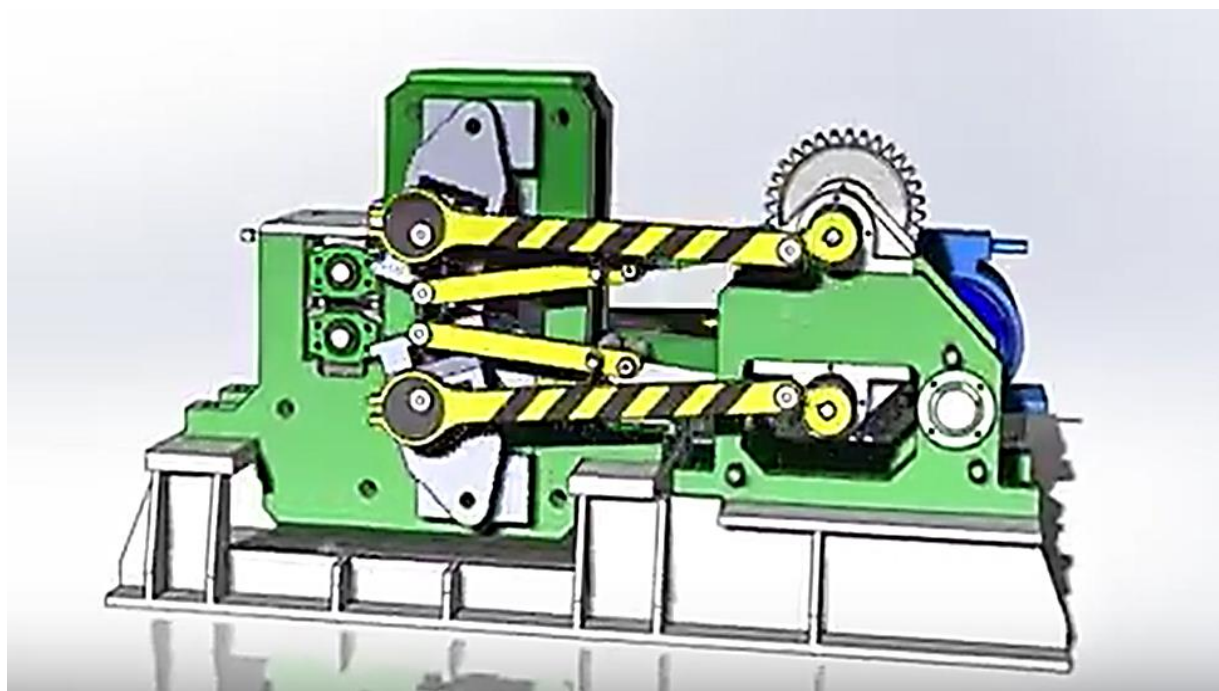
Общий вид маятникового стана с опорным профилированным валком
